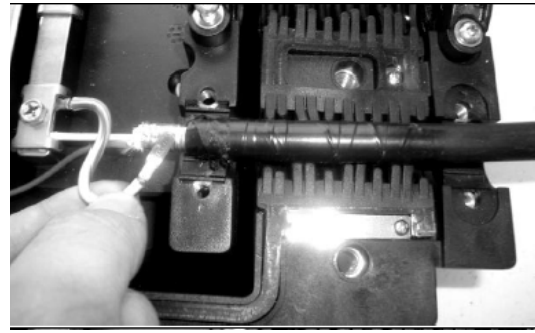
Con ayuda de cinta aislante conectamos el armado del cable con la punta plana del cable de aterrizamiento interno.
